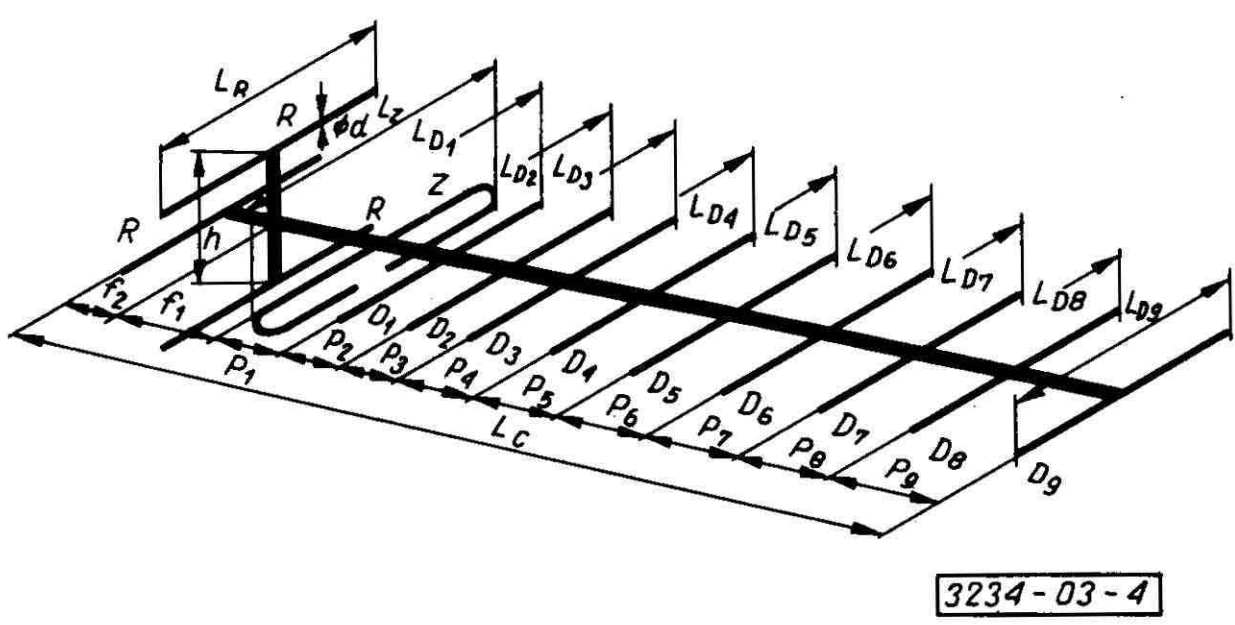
Przykładowa konstrukcja anteny 12-elementowej
